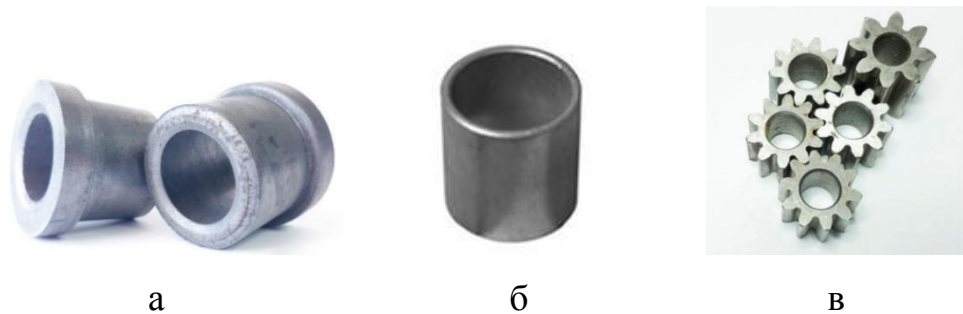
Деталі з антифрикційними властивостями: а - самозмазуючі підшипники; б - втулка; в - шестерні
